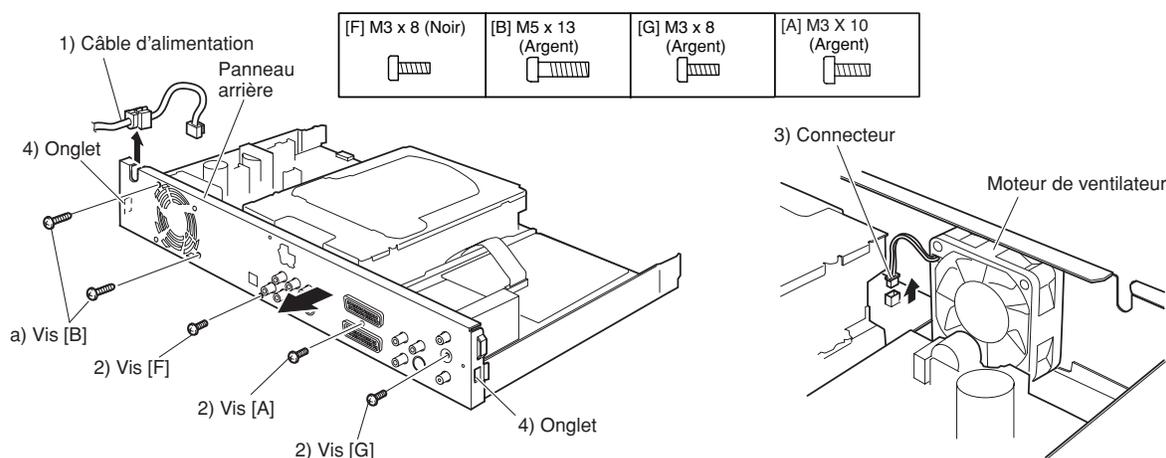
Panneau arrière et moteur de ventilateur
